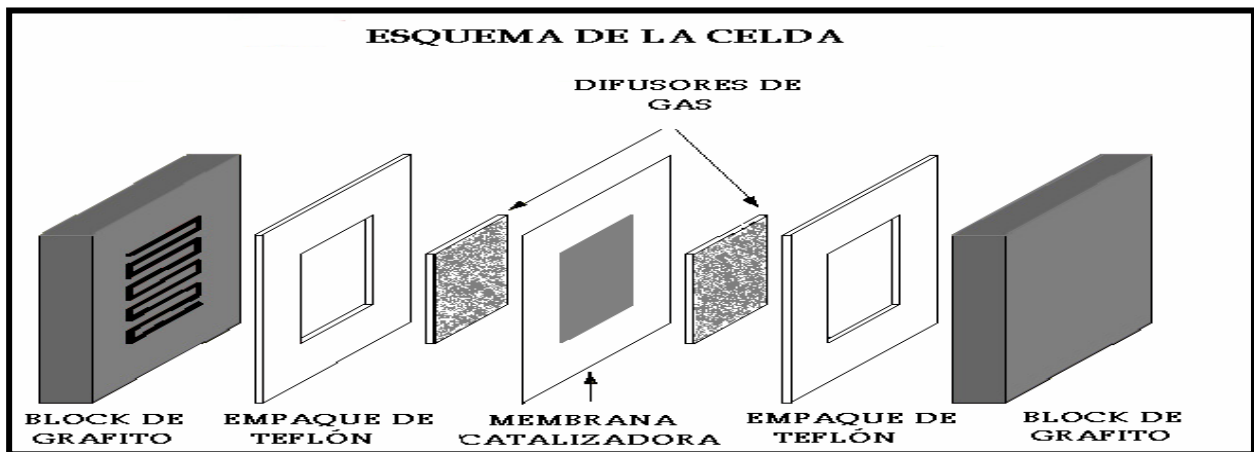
Esquema de las Diferentes Partes y Componentes de una Celda PEM.
